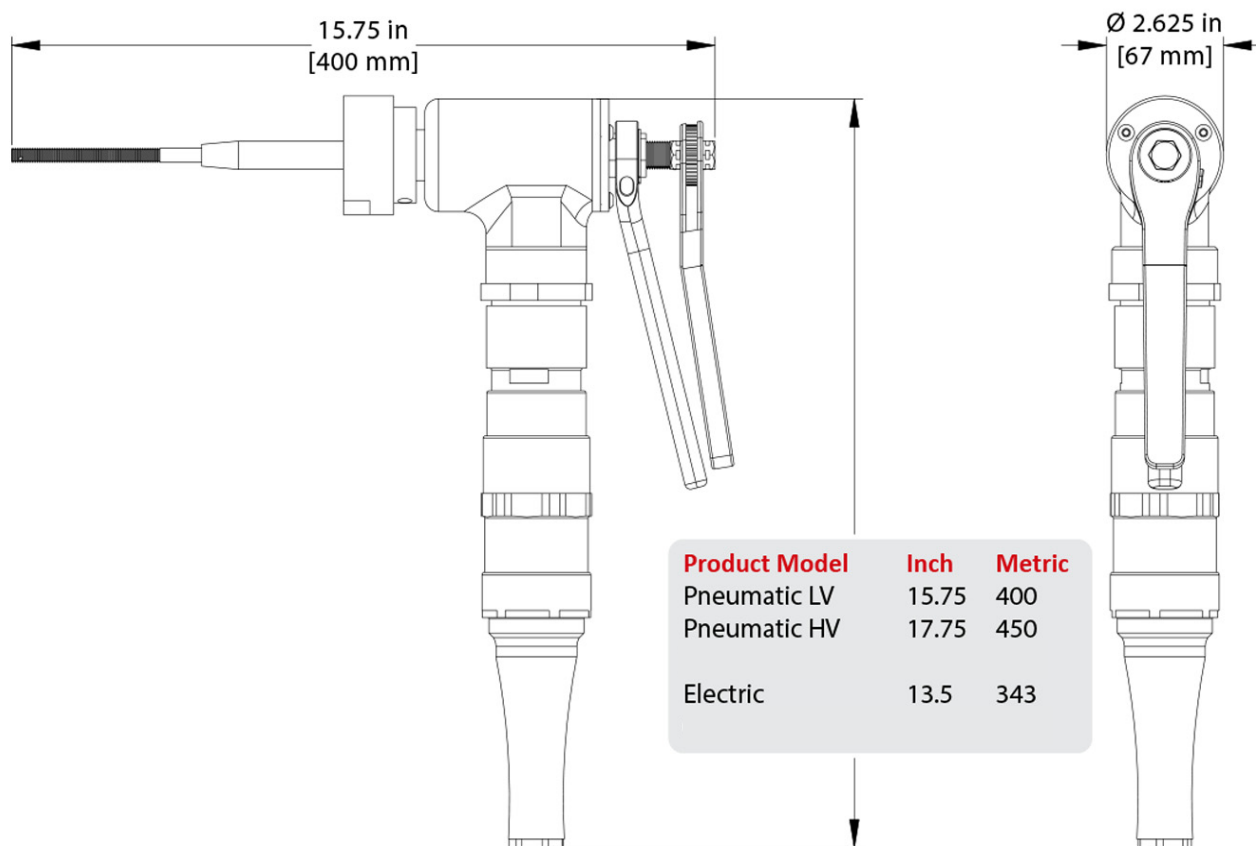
DIMENSIONS DE LA BG38 BOILER GUN
